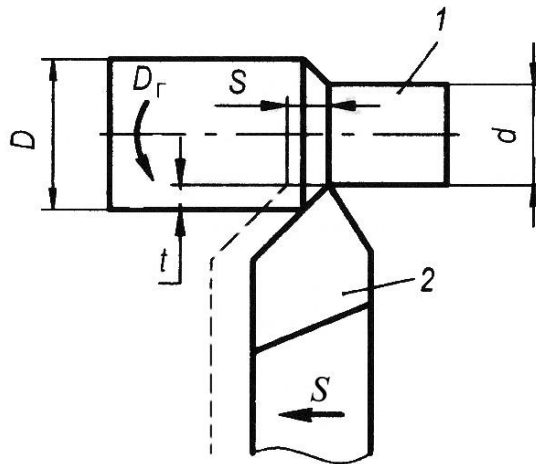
Елементи режиму різання при точінні: 1 – заготовка; 2 – різець; D_r – головний рух різання; S – рух подачі; t – глибина різання; s – подача; D і d – діаметри оброблюваної та обробленої поверхонь
